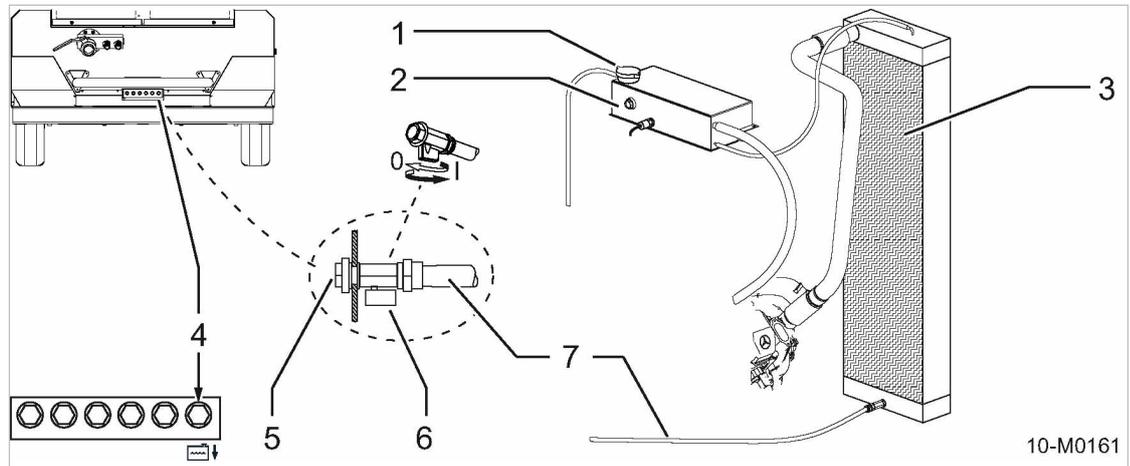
Слив охлаждающей жидкости из радиатора двигателя
